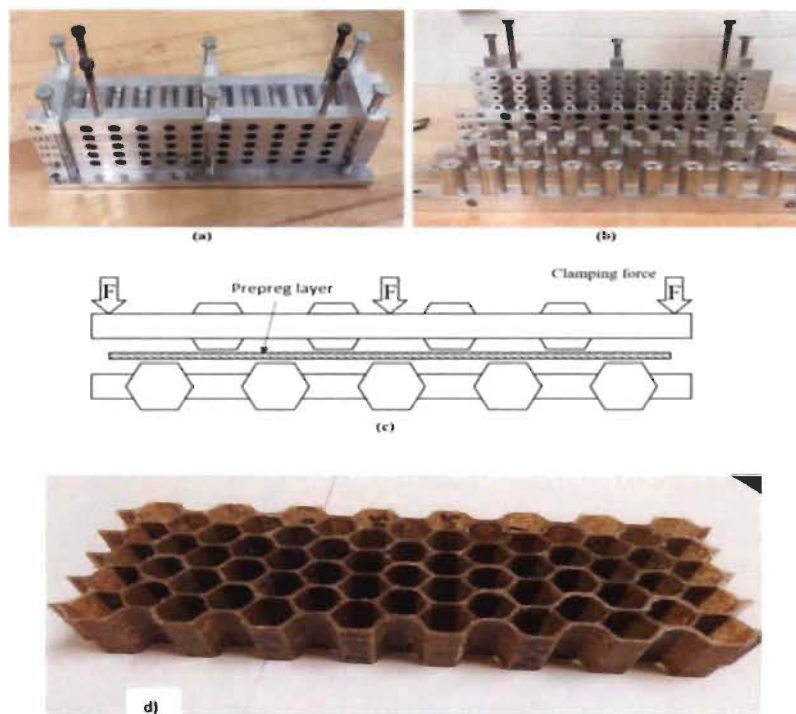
Moule de fabrication de nid d'abeille, a) vue assemblée, b) vue éclatée, c) vue schématique, d) nids d'abeille
